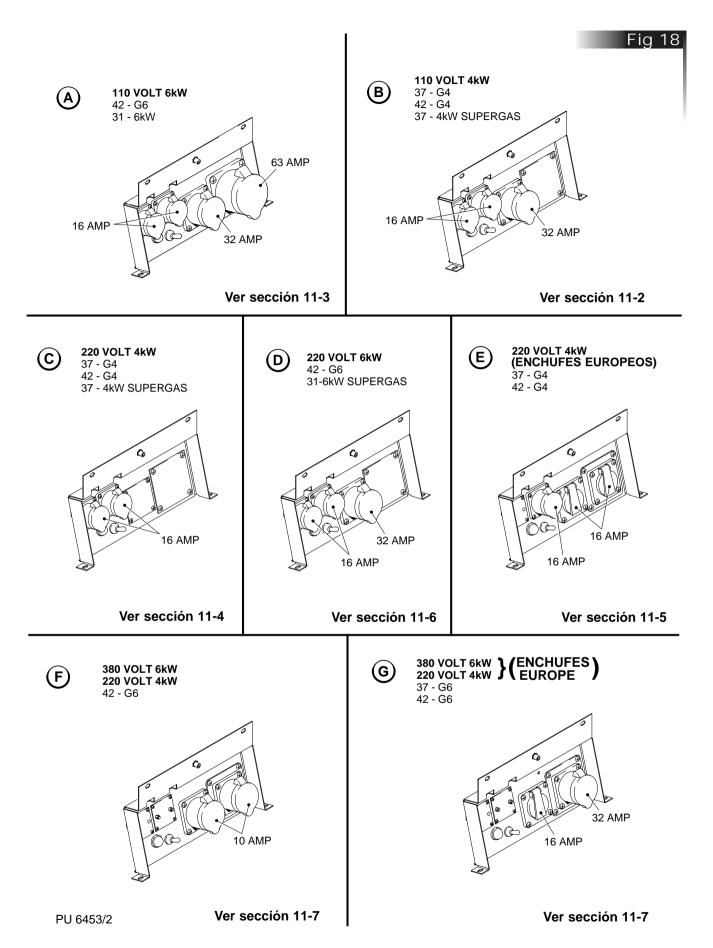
VERSIONES CON ALTERNADOR - CONFIGURACIONES DEL PANEL DE CONTROL
